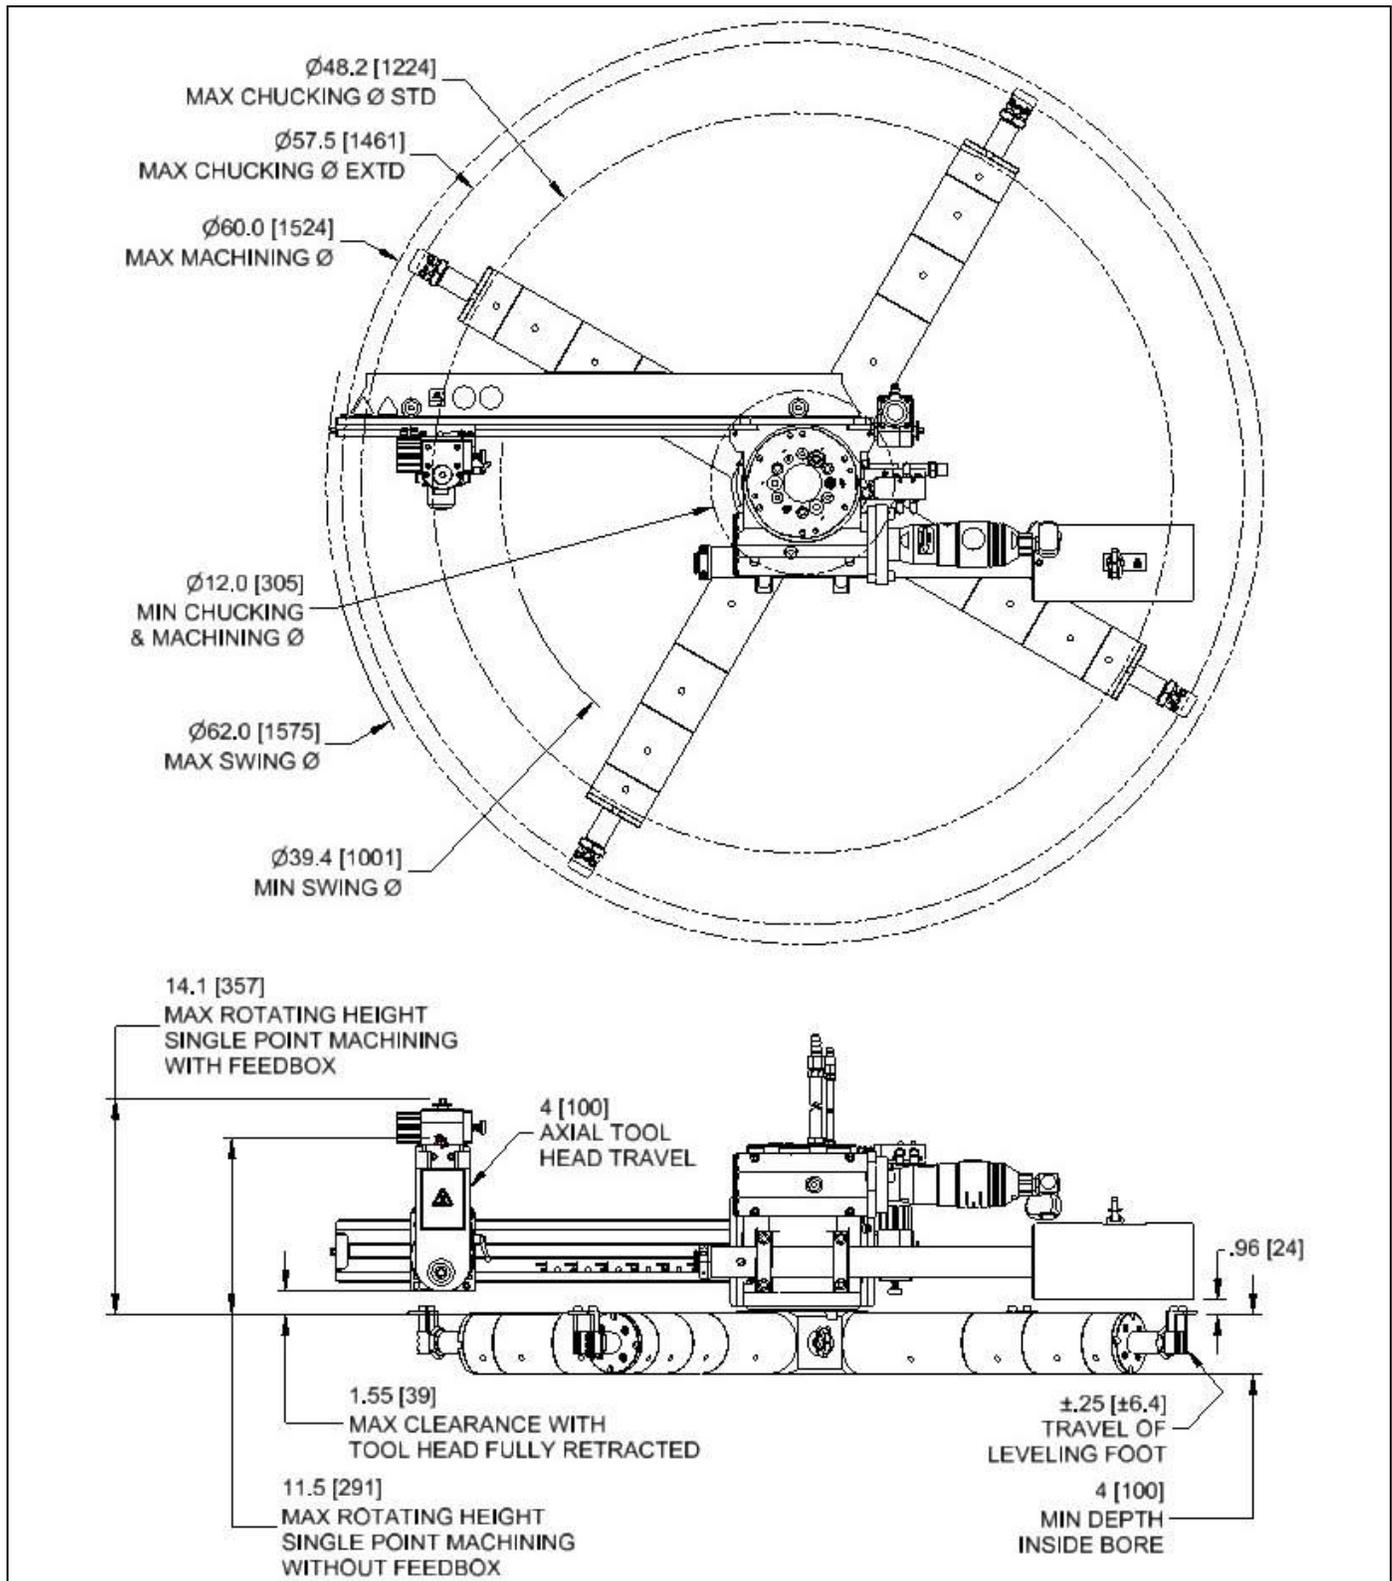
DIMENSIONES DEL ENSAMBLAJE DEL PORTAÚTILES INTERIOR FF6300
